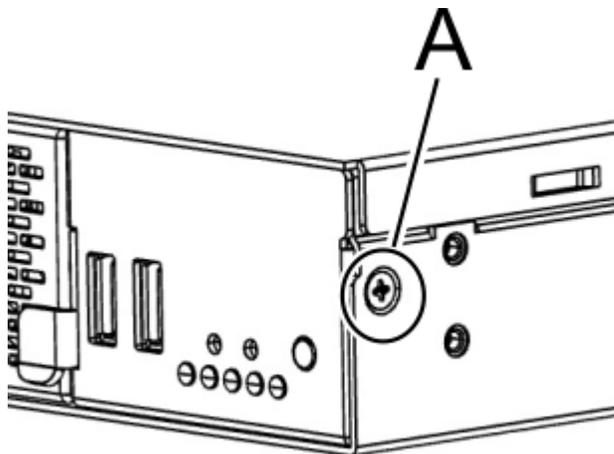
Schraube an der Seite der Steuerkonsole entfernen
